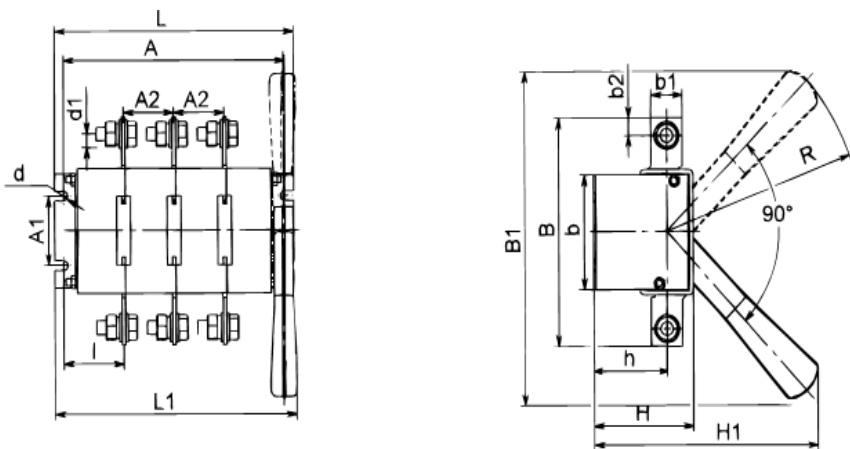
Б Выключатель-разъединитель на одно направление трехполюсный с боковой рукояткой
